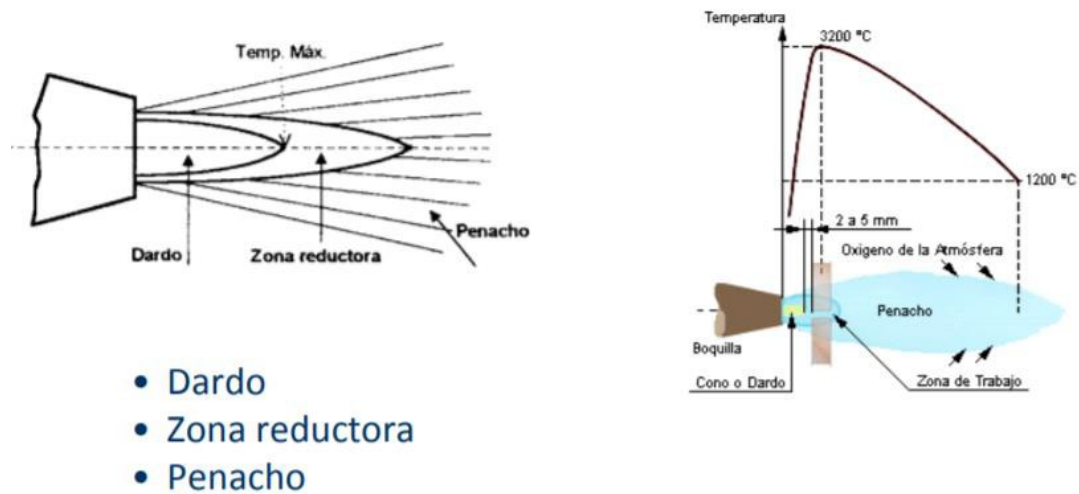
Zonas de la llama del proceso de soldadura oxiacetilénica. [I-38]
